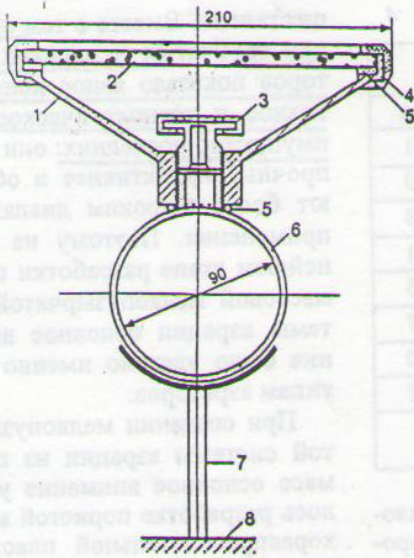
Пластмассовый мелкопузырчатый аэратор НИИ КВОВ с двухслойной пористой пластиной
